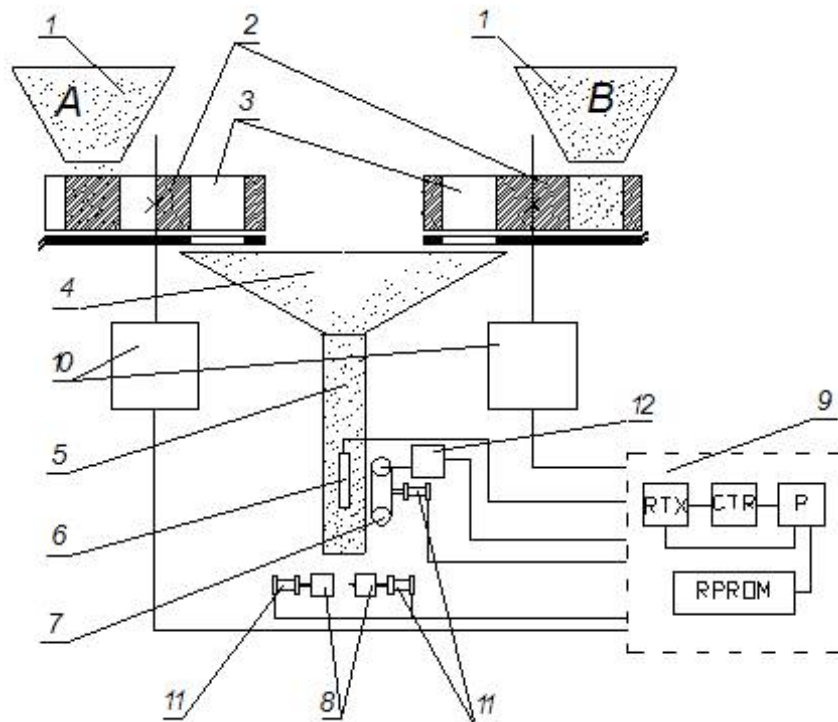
Схема компоновання машини для багатоконпонентного дозування сипких речовин: 1 – бункери; 2 – дозатори; 3 – лоток; 4 – приймальний бункер; 5 – формувальна труба; 6 – губка зварювання поздовжнього шва пакета; 7 – механізм протягування рукава; 8 – губки зварювання поперечних швів пакета; 9 – блок керування; 10 – приводи вивантажування сипких компонент; 11 – пневмоциліндри; 12 – приводи переміщення рукава
